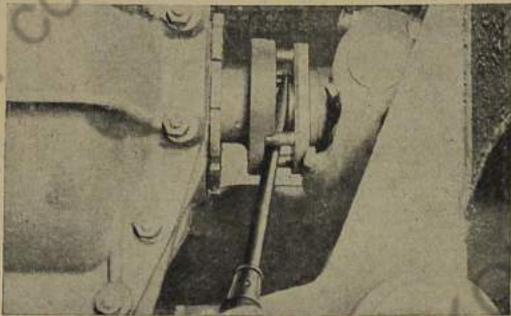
Inneres Kreuzgelenk von Flanschwellen abdrücken
